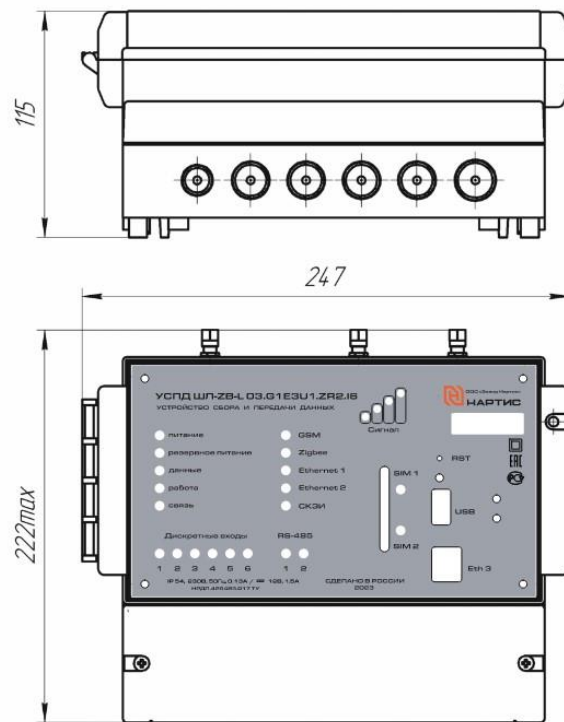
Габаритные и установочные размеры УСПД
